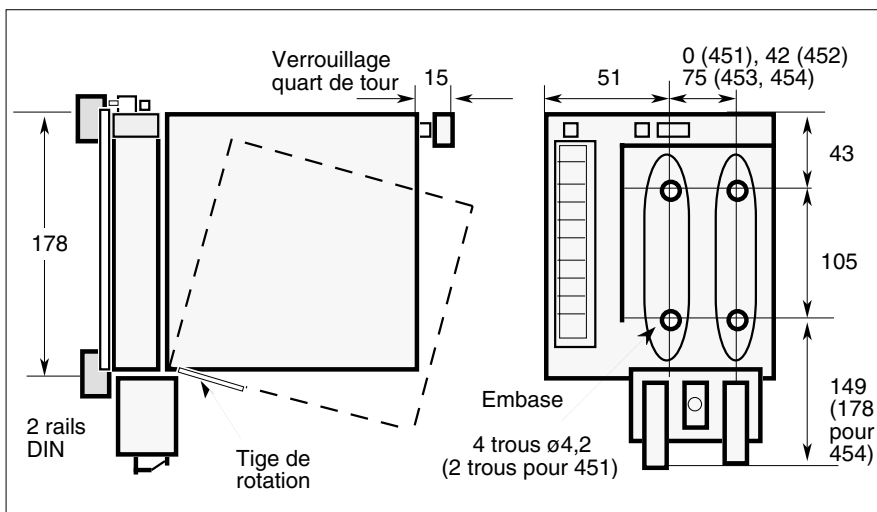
Cotes de fixation sur une paroi verticale (mm)
